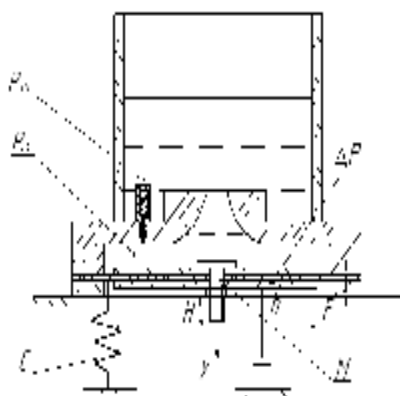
Розрахункова схема робочого органу вібраційної машини
